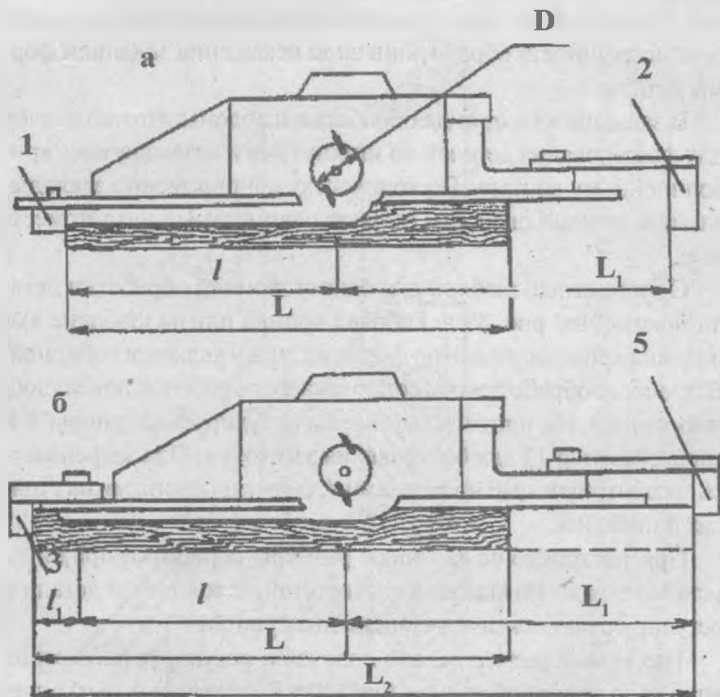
Настройка ограничительных упоров фрезерного станка: а-при обработке паза с выходом на передний торец детали; б-при обработке скрытого паза; 1,3,4-базирующие упоры; 2-предохранительный упор
